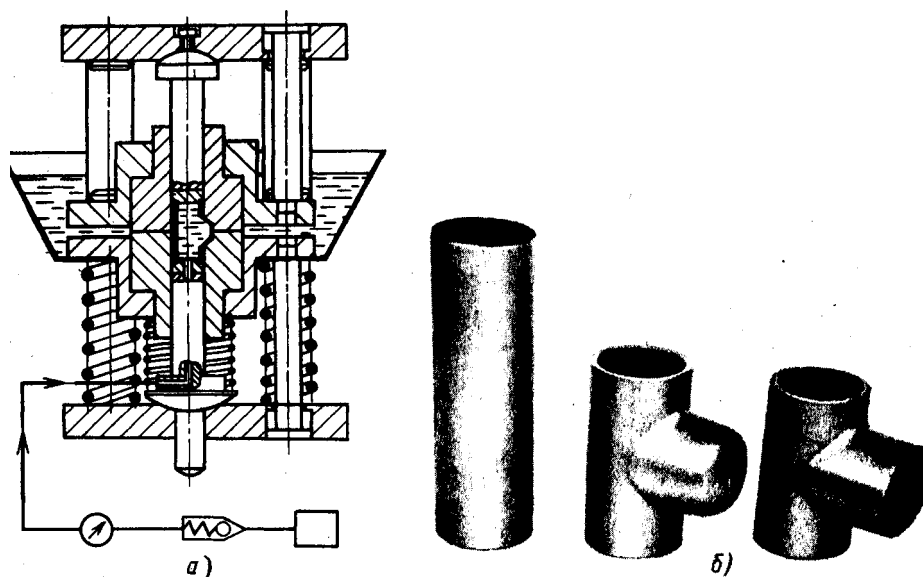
Штамп для изготовления тройника из трубчатой заготовки (а) и технологические переходы изготовления тройника (б)
